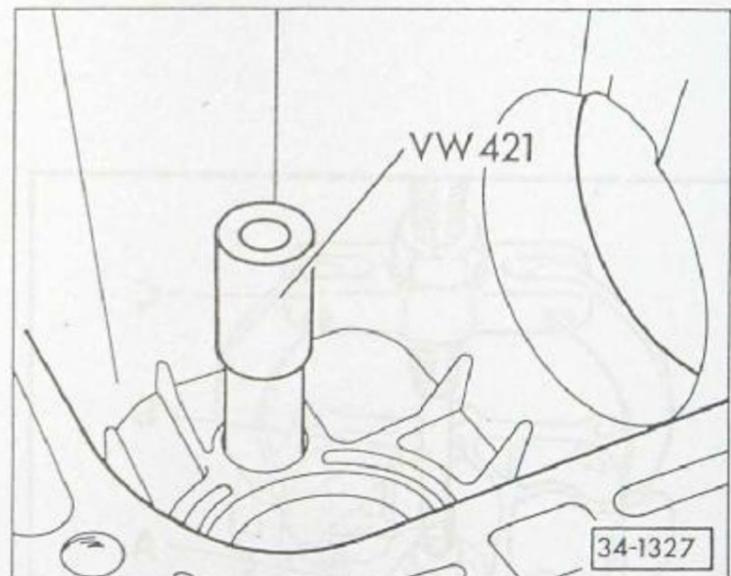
Roulement à aiguilles: extraction du carter de BV
